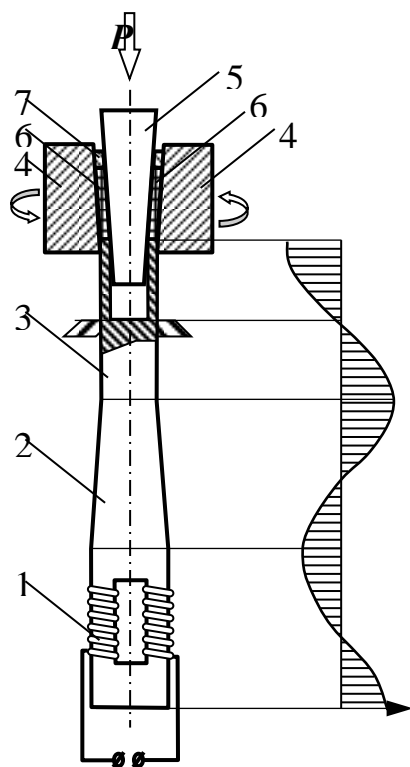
Устройство для t-HPS обработки металлов с наложением ультразвука:
